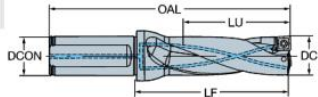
Свердло зі змінними пластинами 880-D6000L40-02 та його геометричні параметри
